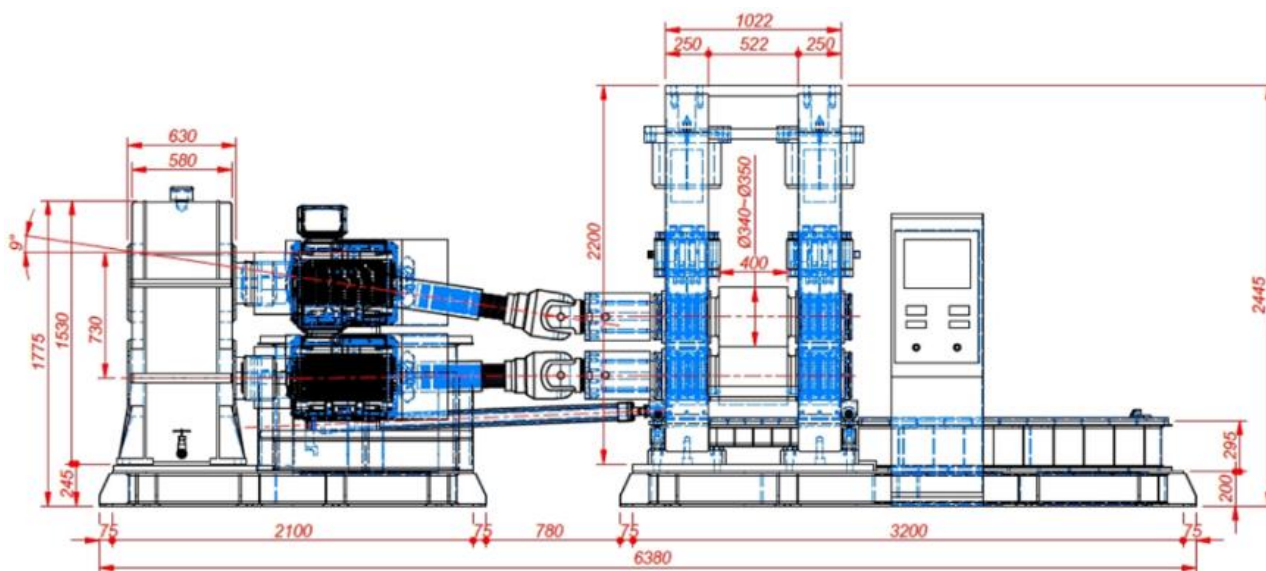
Габаритные размеры опытно-экспериментального лабораторного стана дуо с индивидуальным приводом рабочих валков
